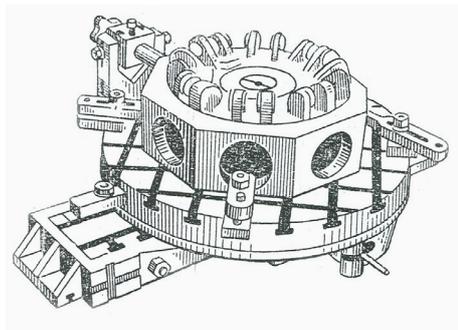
Приспособление, собранное из элементов УСП для фрезерования
